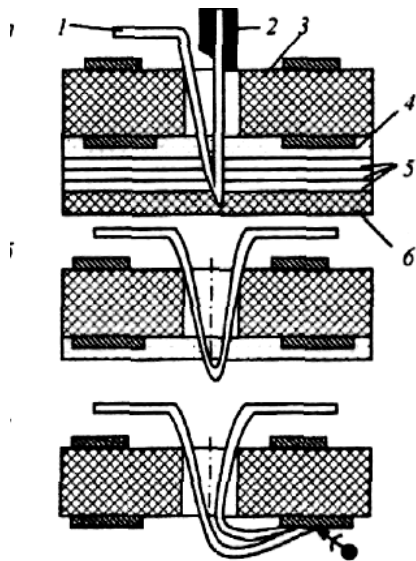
Схема стежкового монтажа: 1 – провод, 2 – игла, 3 – плата, 4 – кабельная бумага, 5 – пакет резиновых прокладок, 6 – защитный слой
